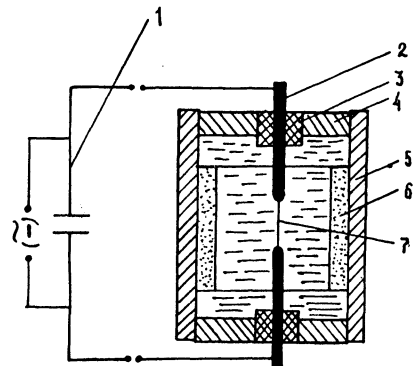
Схема электрогидравлического прессования порошковой полый заготовки:
